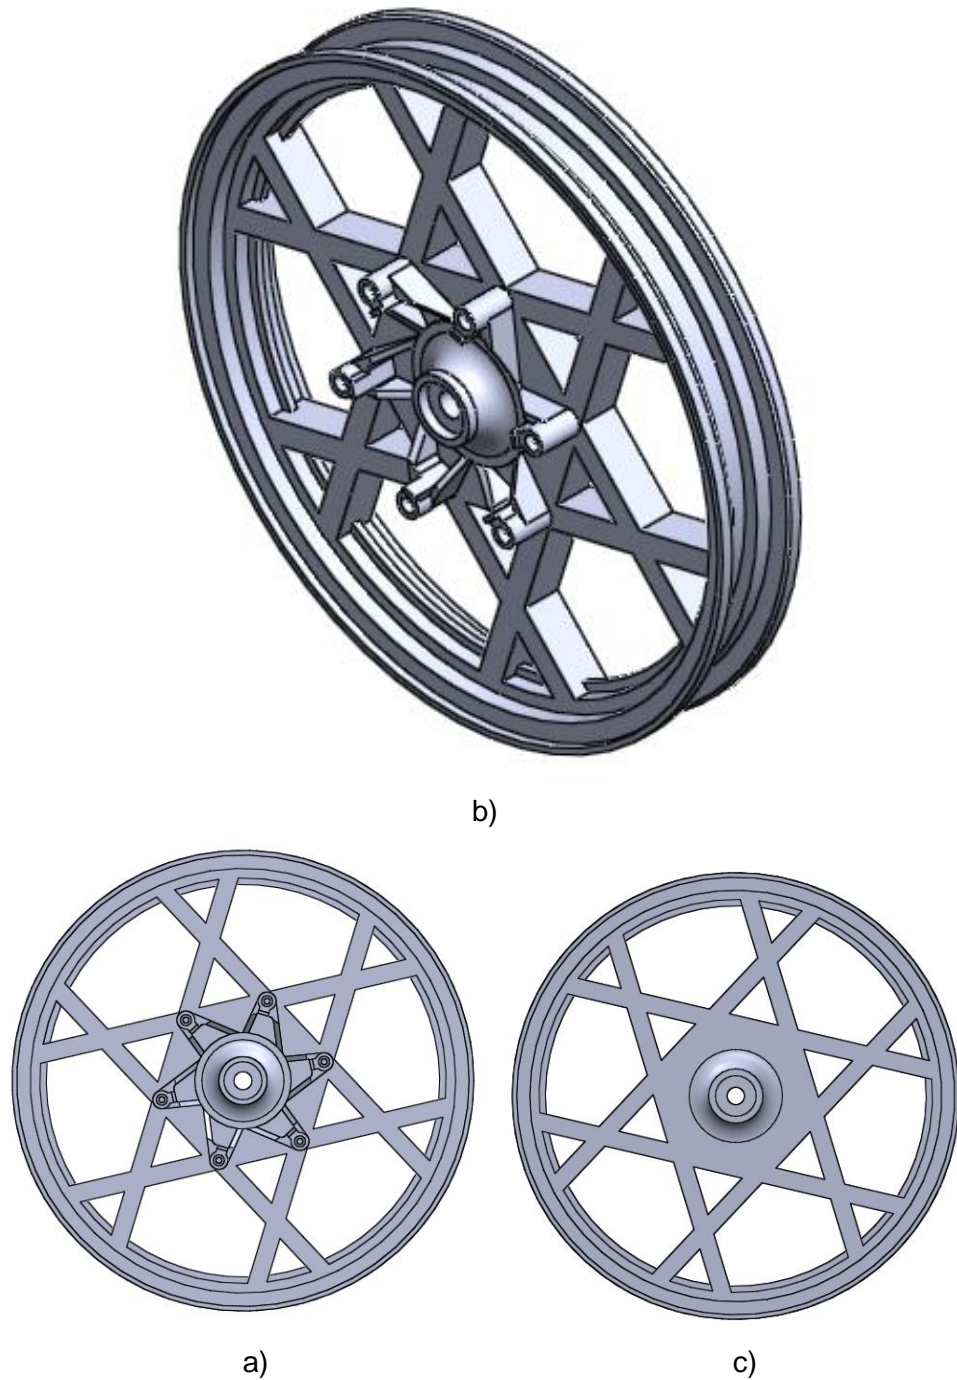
Diseño descartado “c.3” a) Vista frontal. b) Vista isométrica. c) Vista trasera.
